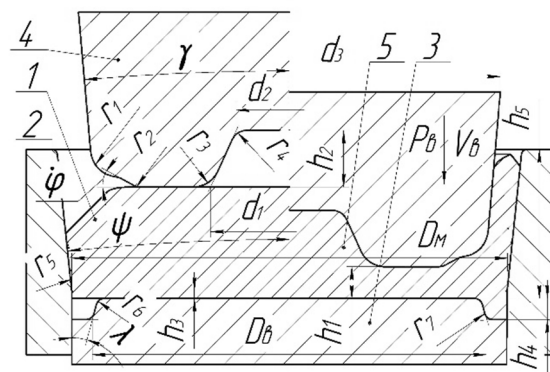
Схема гарячого зворотного видавлювання з роздачою: 1 – заготовка, 2 – матриця, 3 – плита, 4 – пуансон, 5 – напівфабрикат
